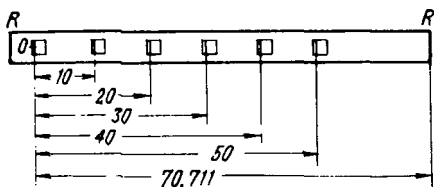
Малая координатная линейка Ф. В. Дробышева
